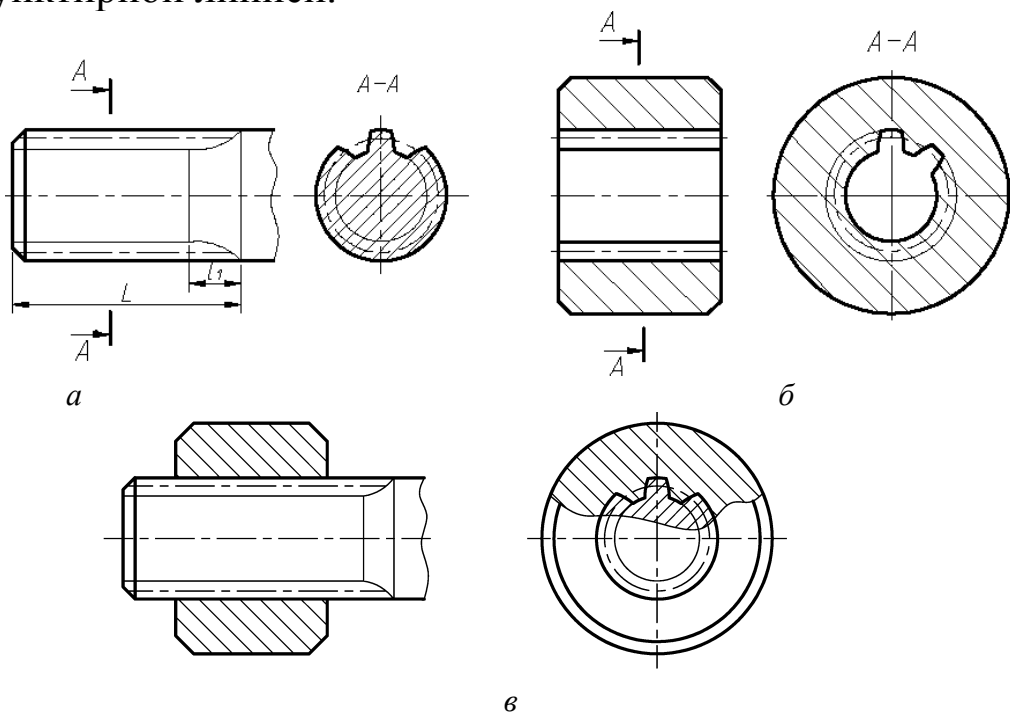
Изображение шлицевых деталей с эвольвентным профилем зуба:
